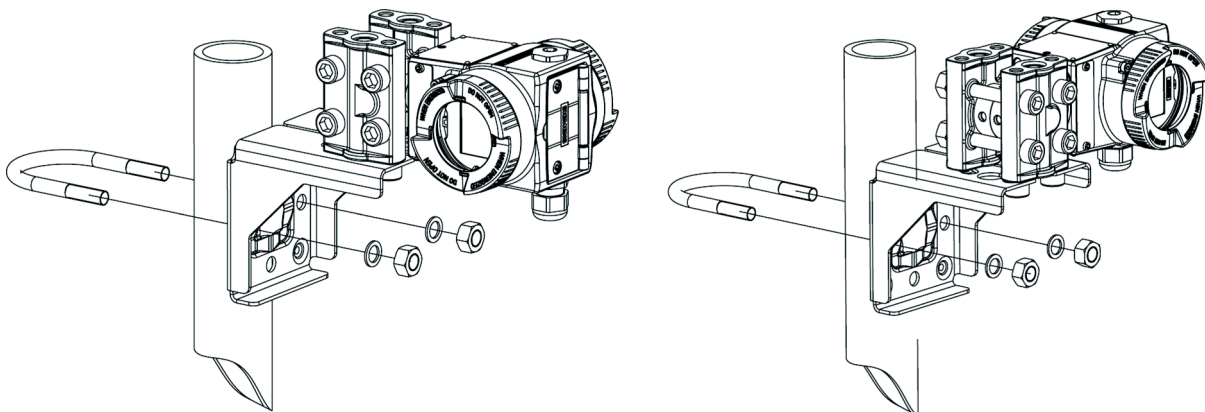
Befestigung des Messumformers mit Montagewinkel für senkrechte Wirkdruckleitungen
